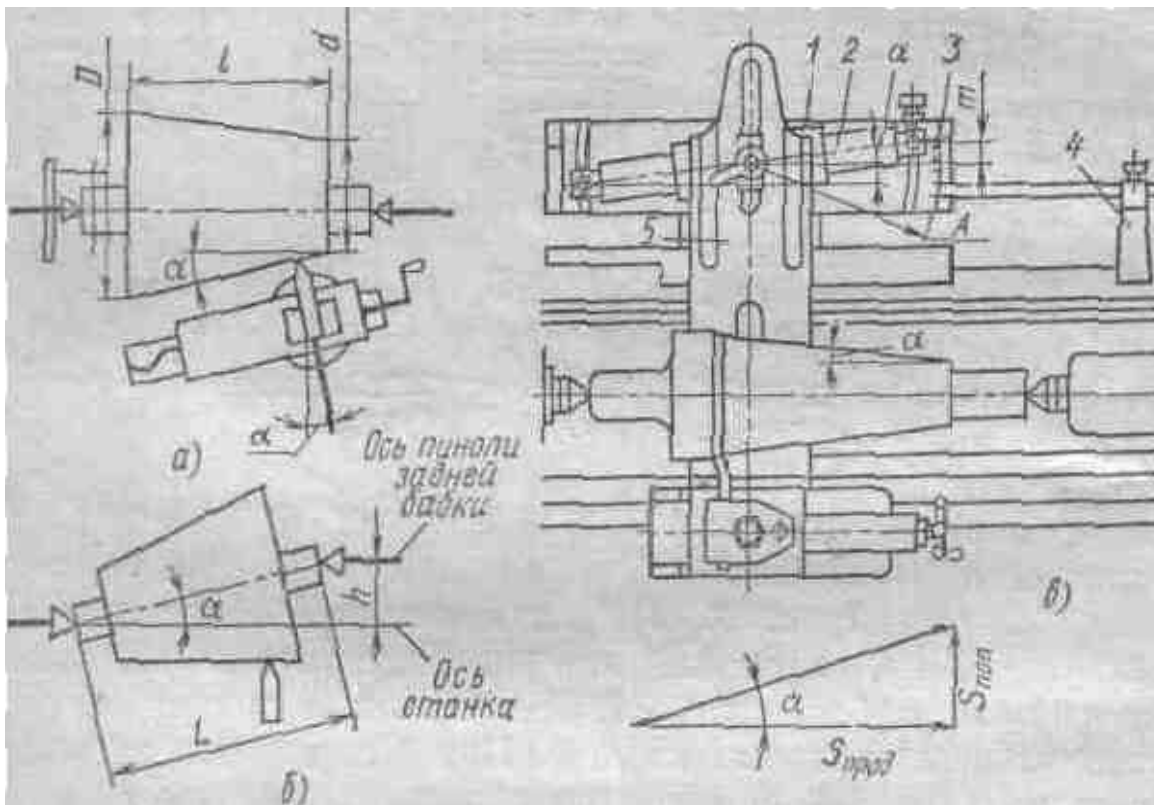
Схема обработки конусов на токарно-винторезном станке
